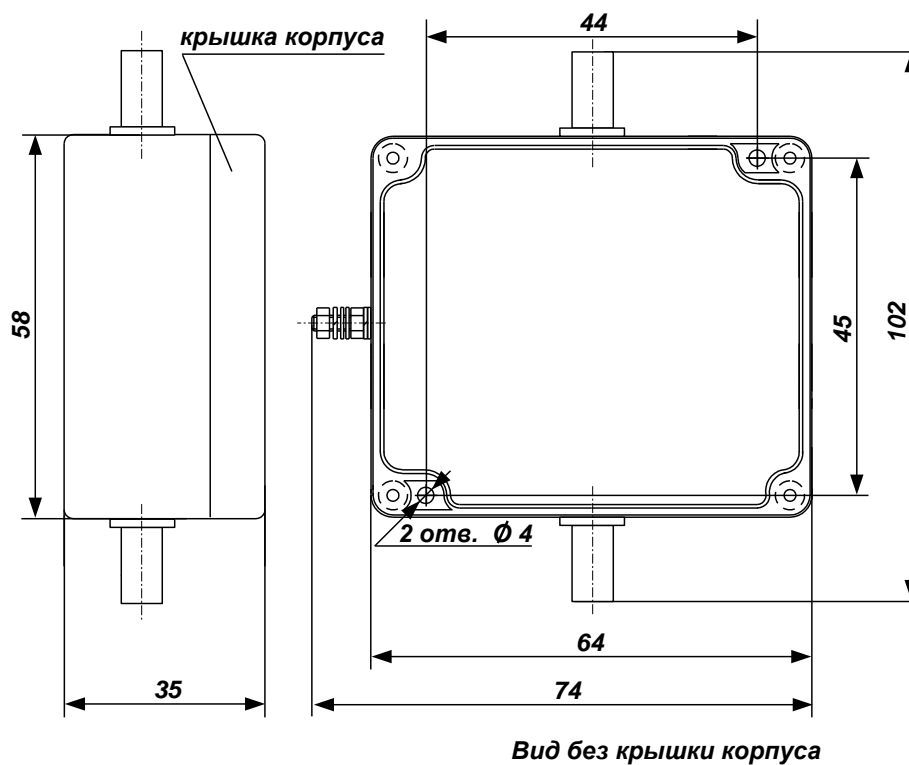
Габаритные и присоединительные размеры БЗВВ-01
